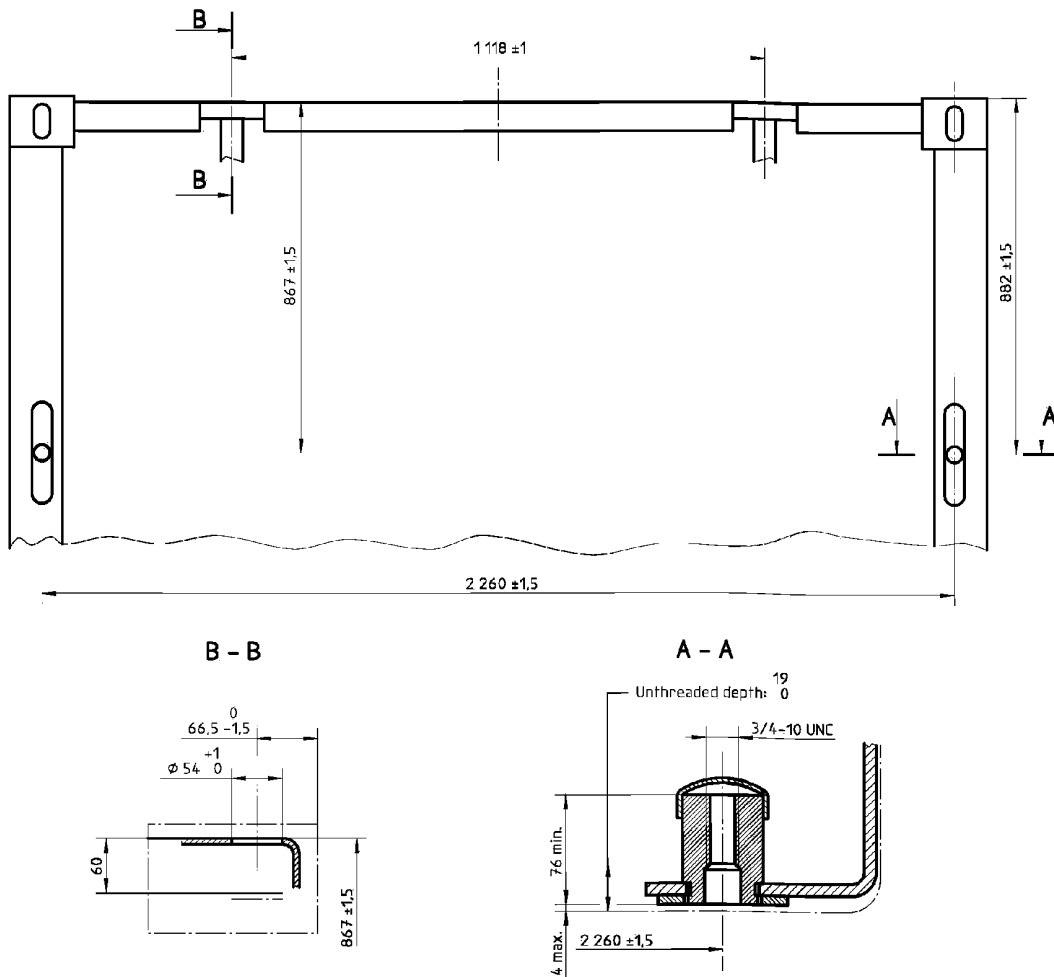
Расположение и размеры гнезд для крепления навесного генератора
